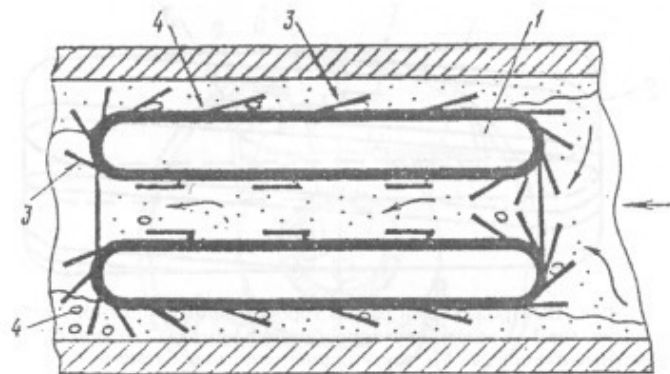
Общий вид торообразного очистного устройства, где 2 – лента; 3 – стержни очистных элементов.
